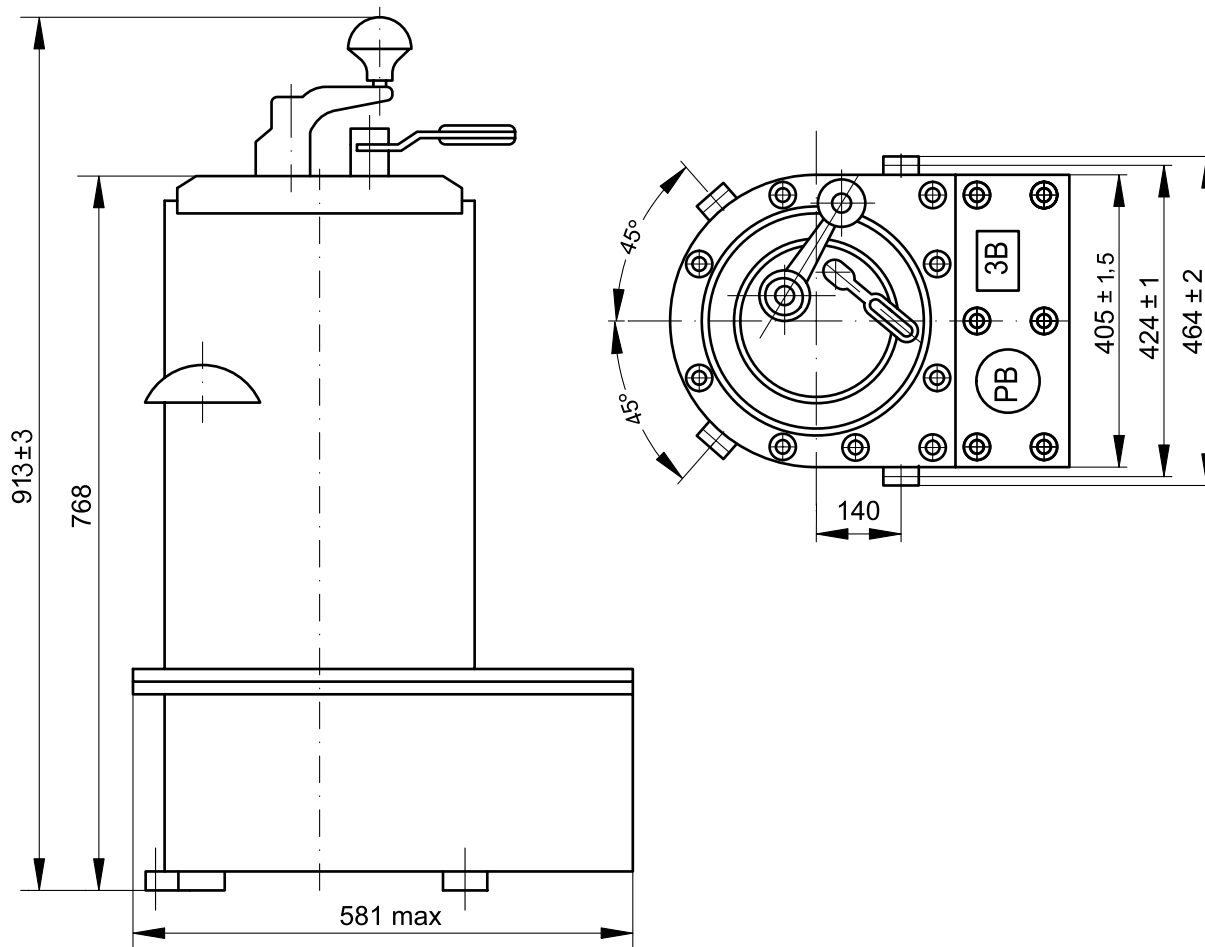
Габаритные и установочные размеры контроллера КРВ–2М
